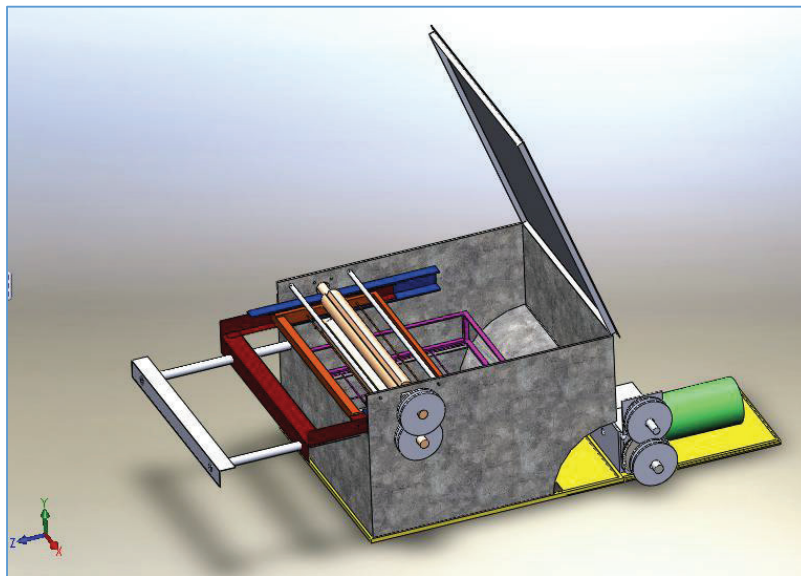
MÁQUINA ENSAMBLADA COMPLETA
